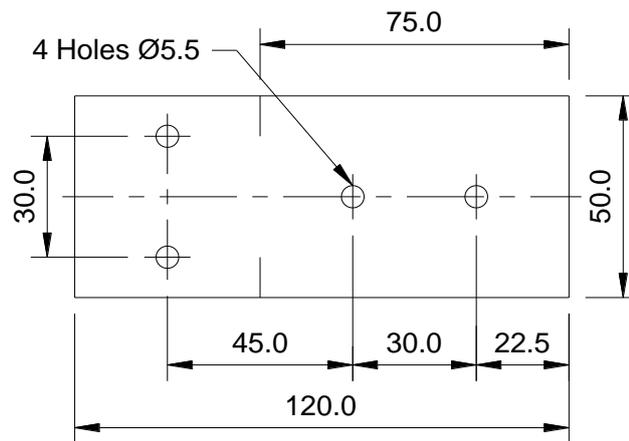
19 Plantilla para perforaciones de crack meter
